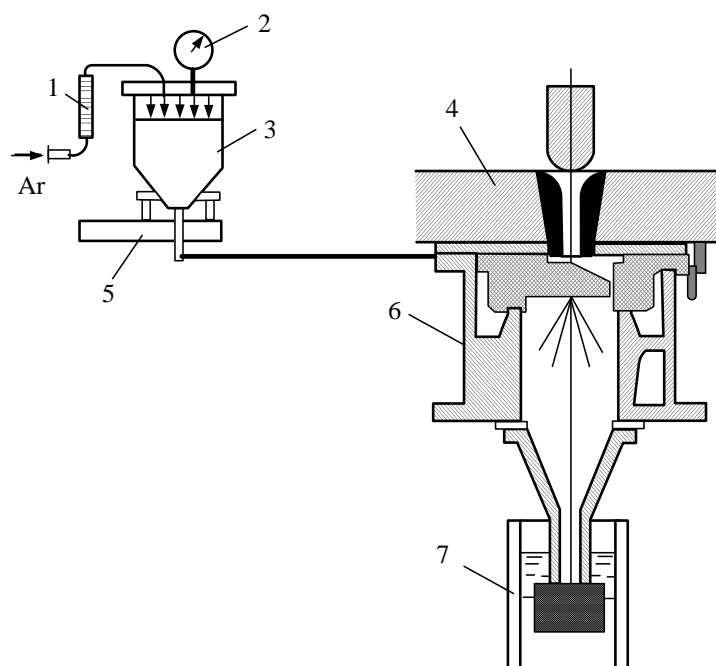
Схема устройства для введения металлического порошка в струю металла при непрерывной разливке: 1 – измеритель скорости подачи аргона; 2 – манометр; 3 – контейнер с порошком; 4 – промежуточный ковш; 5 – месдоза; 6 – погружной стакан специальной конструкции; 7 – кристаллизатор
